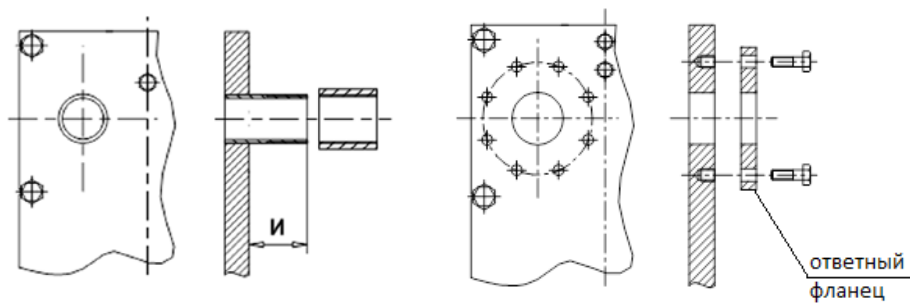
Схема установки теплообменника на фундаментную раму
